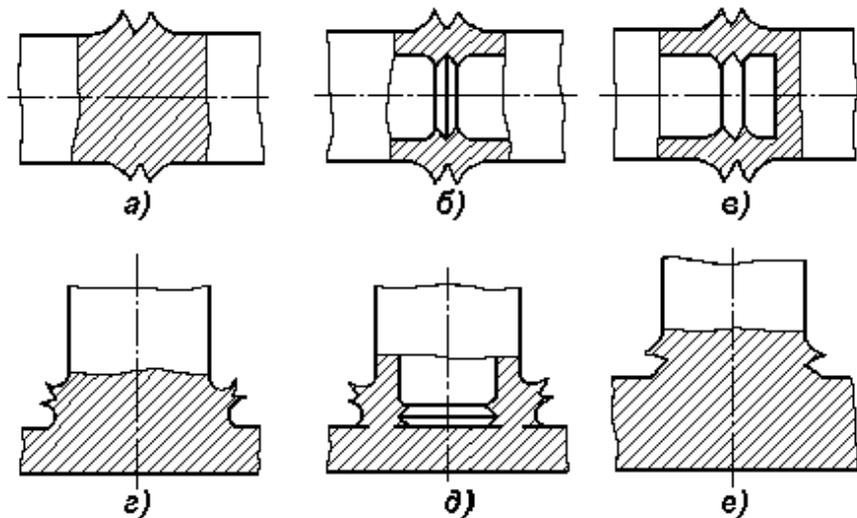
Типы сварных соединений, выполняемых сваркой трением
